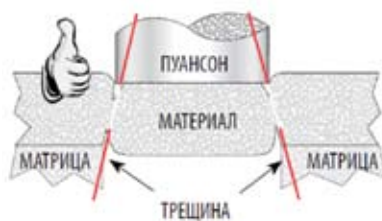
б. Соответствующий зазор – образование равномерной трещины, баланс между усилием штамповки, качеством обраб. детали и сроком службы инструмента
